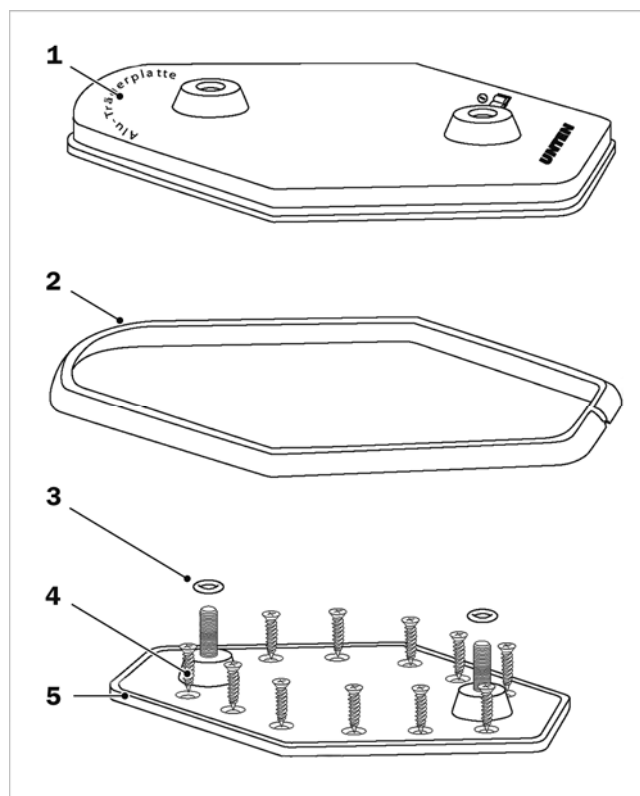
volume de livraison de la fixation sur toiture ADH-SF
